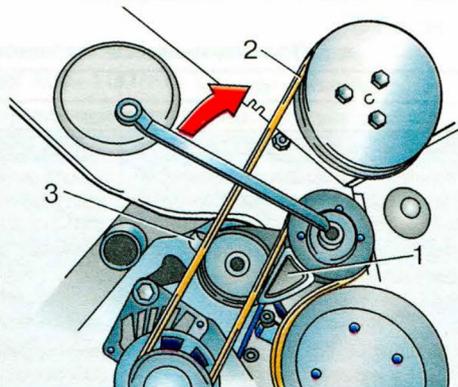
Ослабление натяжения ремня привода агрегатов 6-цилиндрового двигателя: 1 – механизм натяжения ремня привода агрегатов; 2 – ремень привода агрегатов; 3 – штифт фиксирующий
